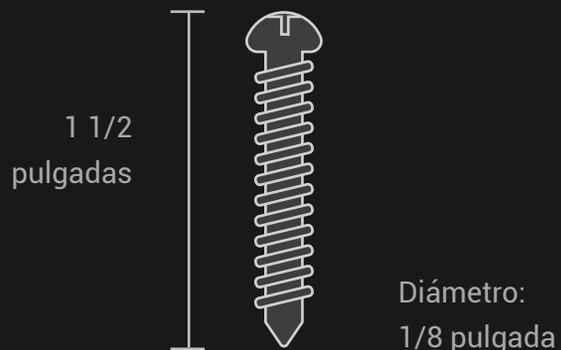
Tipo de tornillo utilizado en el ensamblaje de carcasa
